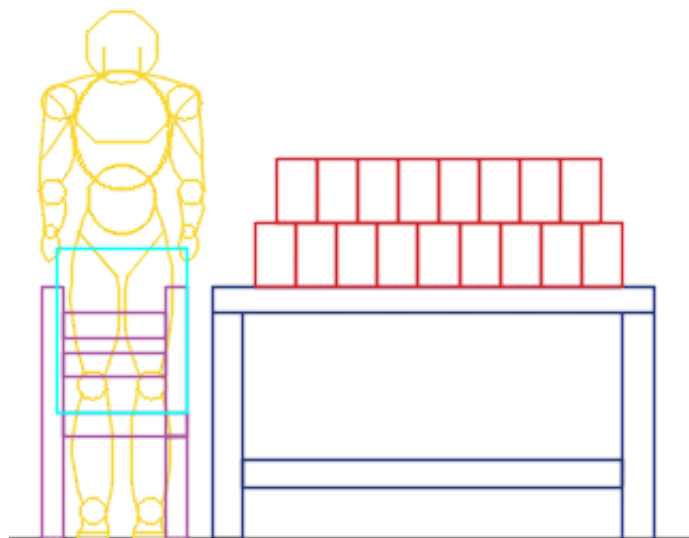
Puesto de trabajo de empaquetado – Vista frontal actual
